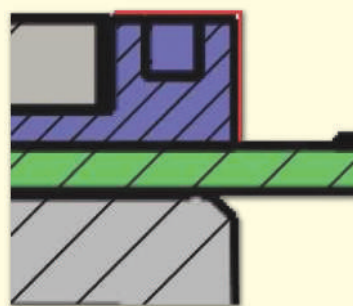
Поперечний переріз зі шляхами струмів витоку від «тонкої» притисної кришки до PCB
